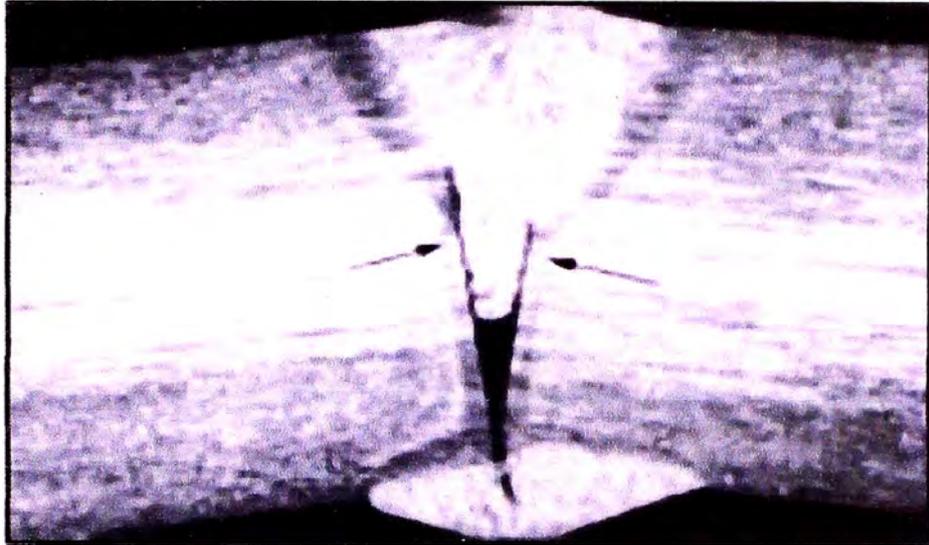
Falta de Fusión entre el metal de soldadura y el metal base
